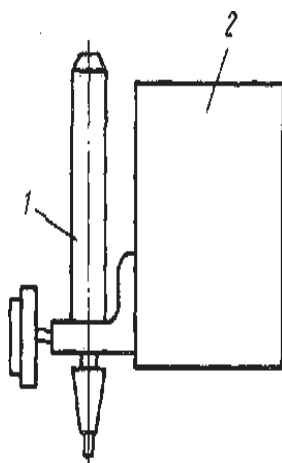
Конструкция пишущего узла чертежного автомата: 1 — пишущее устройство;
